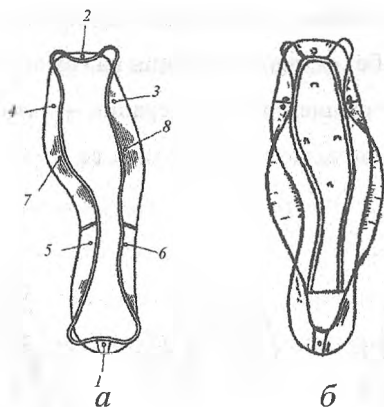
Обтяжка заготовки: *а* – клеевого метода крепления; *б* –
